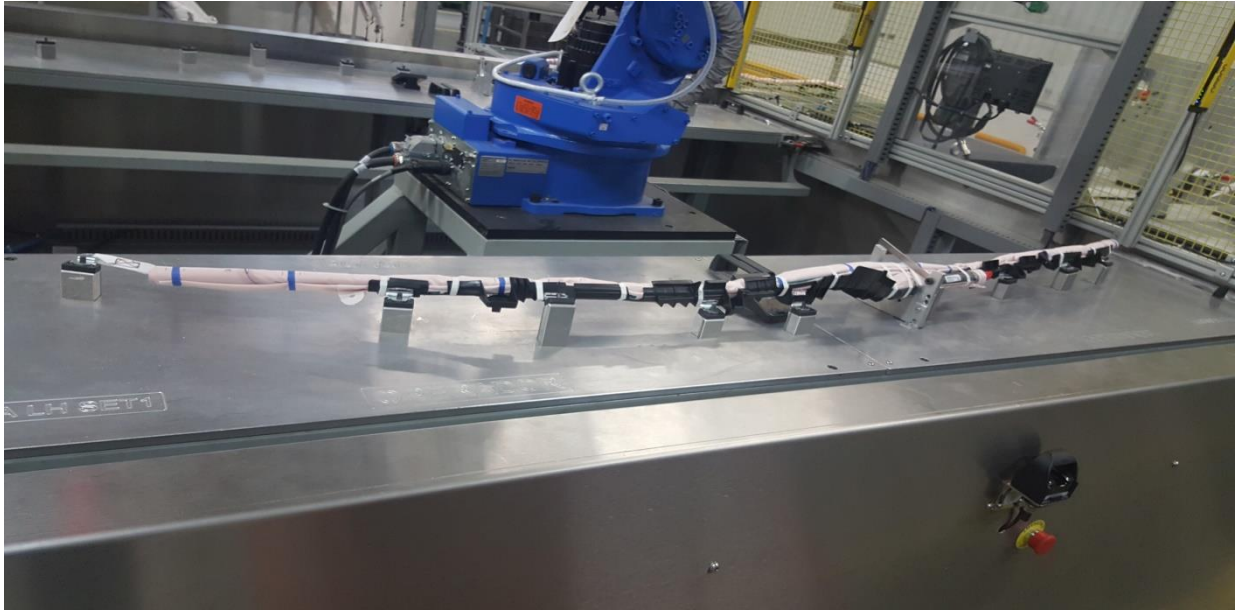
fixture para colocar las bolsas de cortina para inspección visual final
